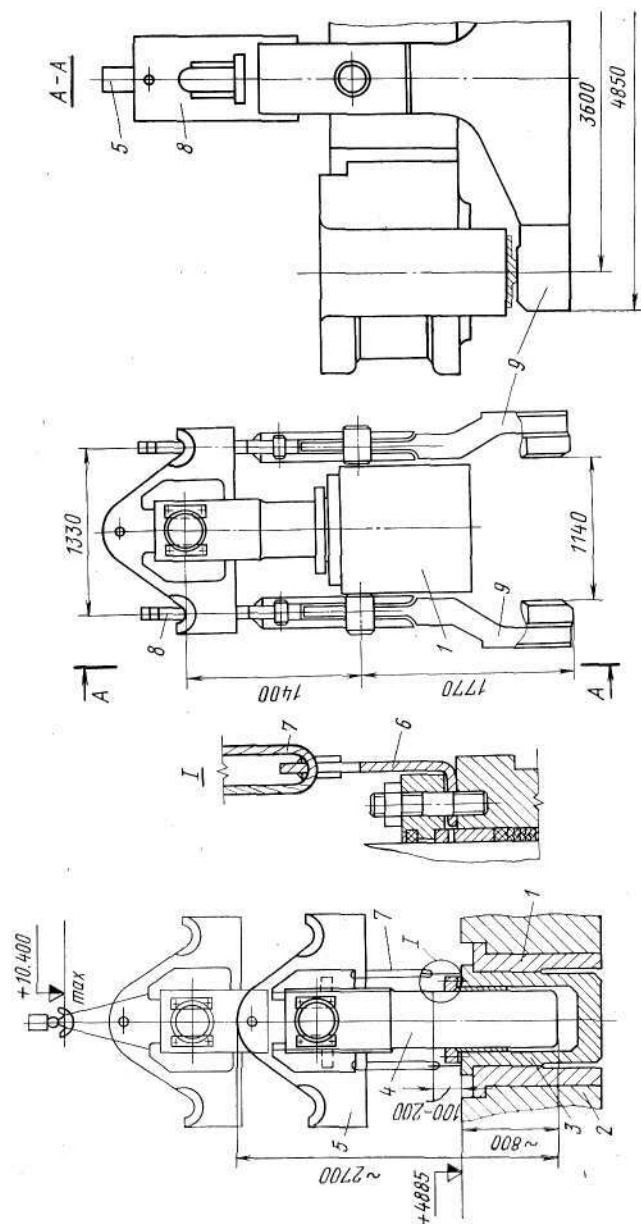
Схема монтажа механизма уравновешивания верхнего опорного вала
